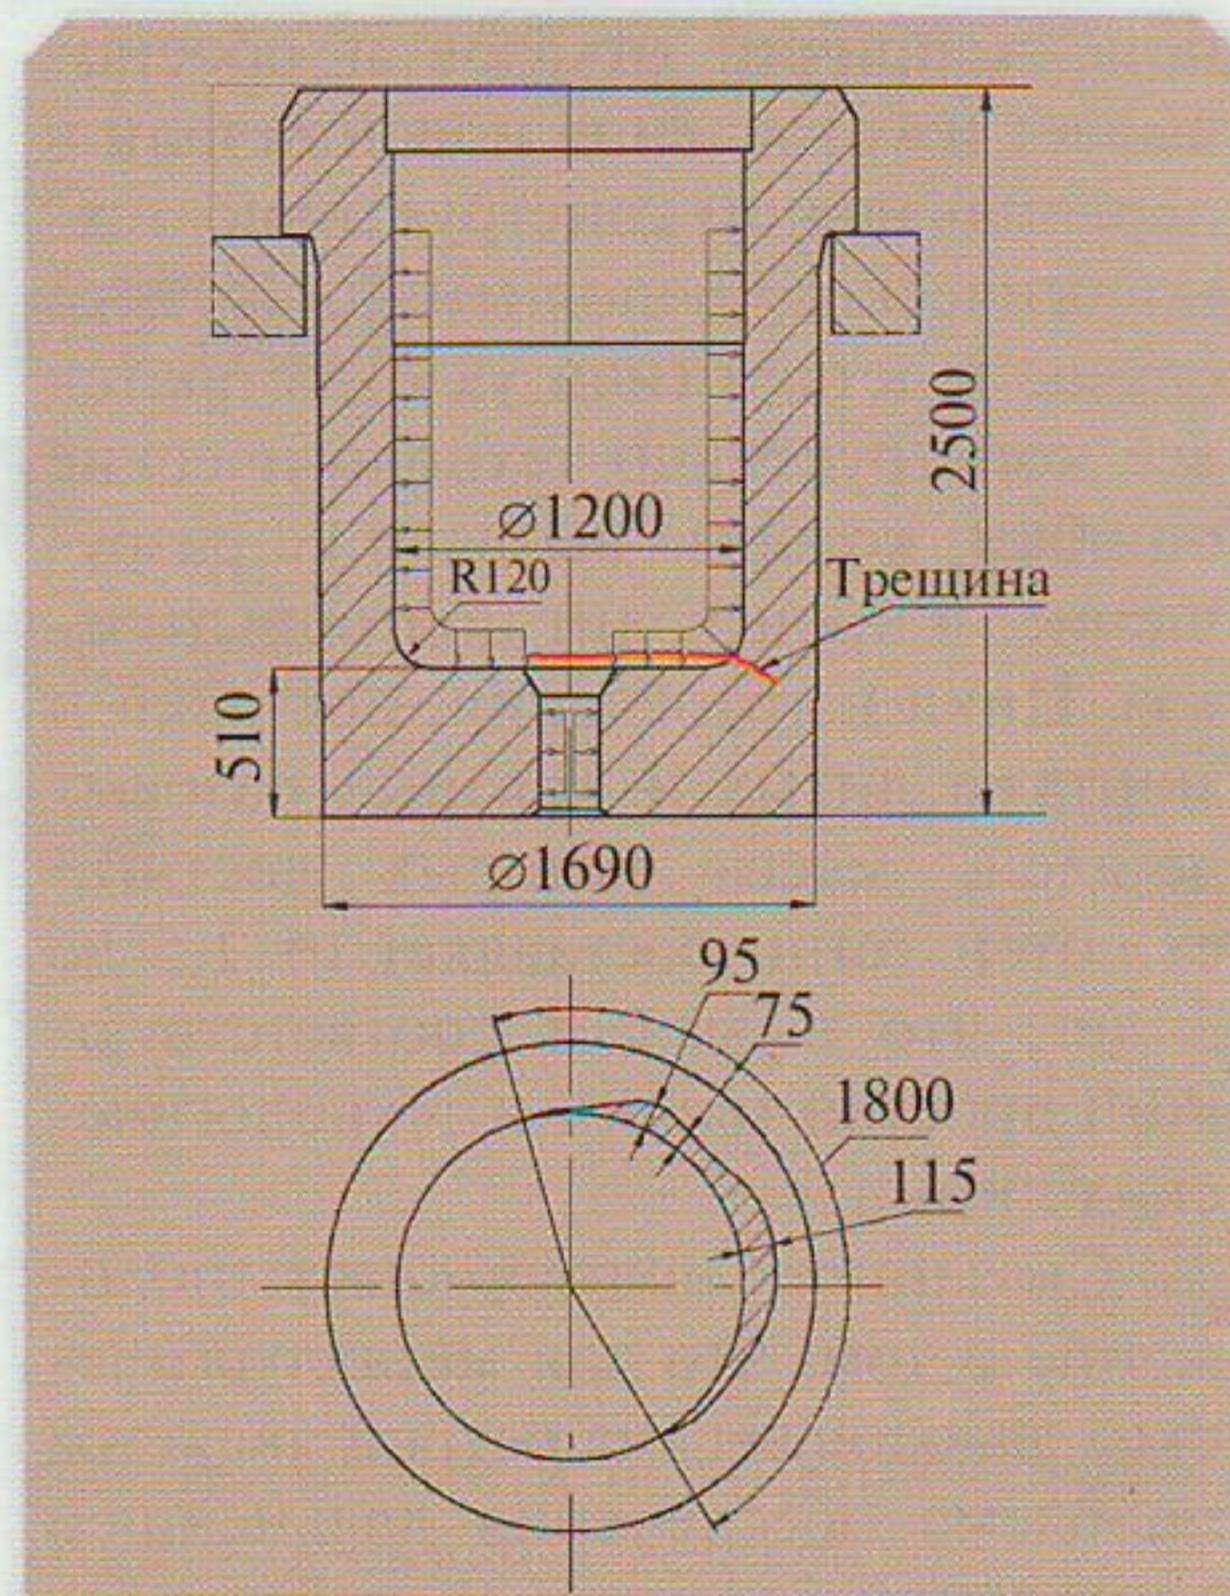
Схема расположения и размер трещины в днище цилиндра силой 35 МН
